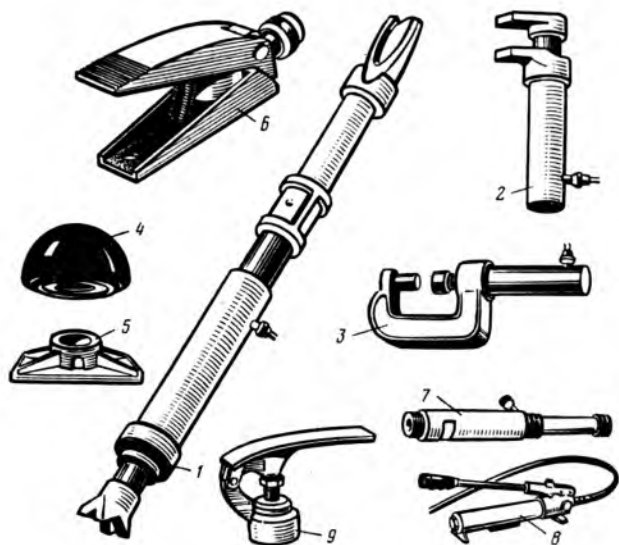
Набор приспособлений для устранения деформаций кузова: 1 — гидравлический цилиндр с удлинительной трубкой и плунжером; 2, 3 — гидравлические струбины; 4 — резиновая головка; 5 — опорная головка; 6 — гидравлический клин; 7 — натяжной цилиндр; 8 — гидравлический насос; 9 — лопатообразная головка
